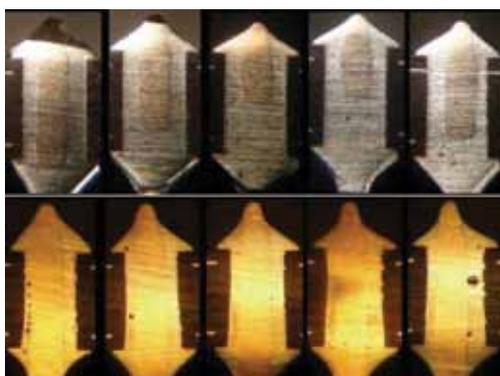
Поперечное сечение ПУ спаянного на установке Б
